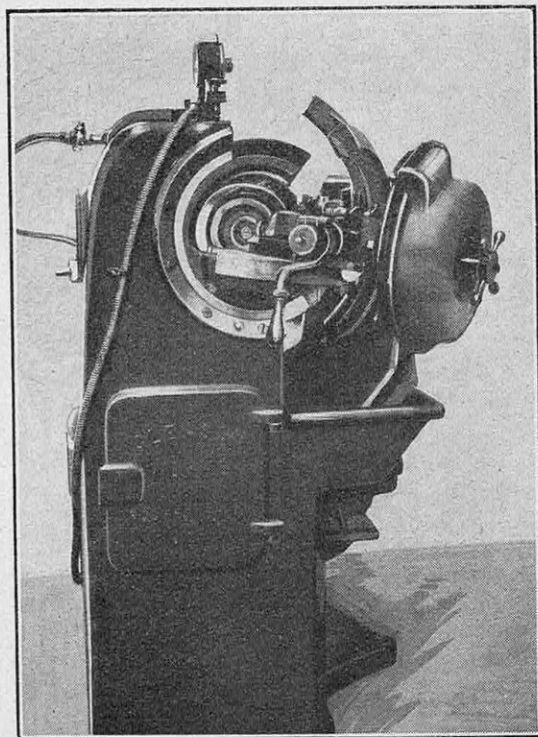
MACHINE A TAILLER LES ENGRENAGES CONIQUES DE FORME SPIRALE
